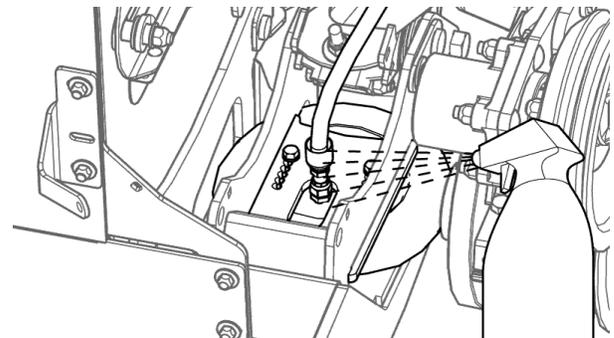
Compruebe si hay fugas en las bolsas de aire del bastidor auxiliar
